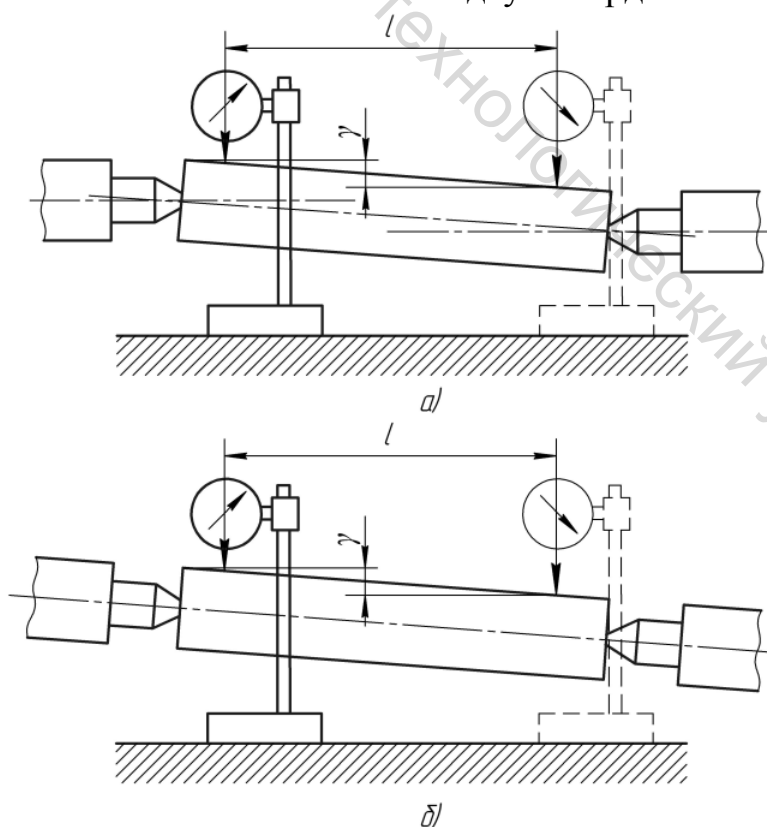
Проверка соосности центров токарного станка с помощью оп-
